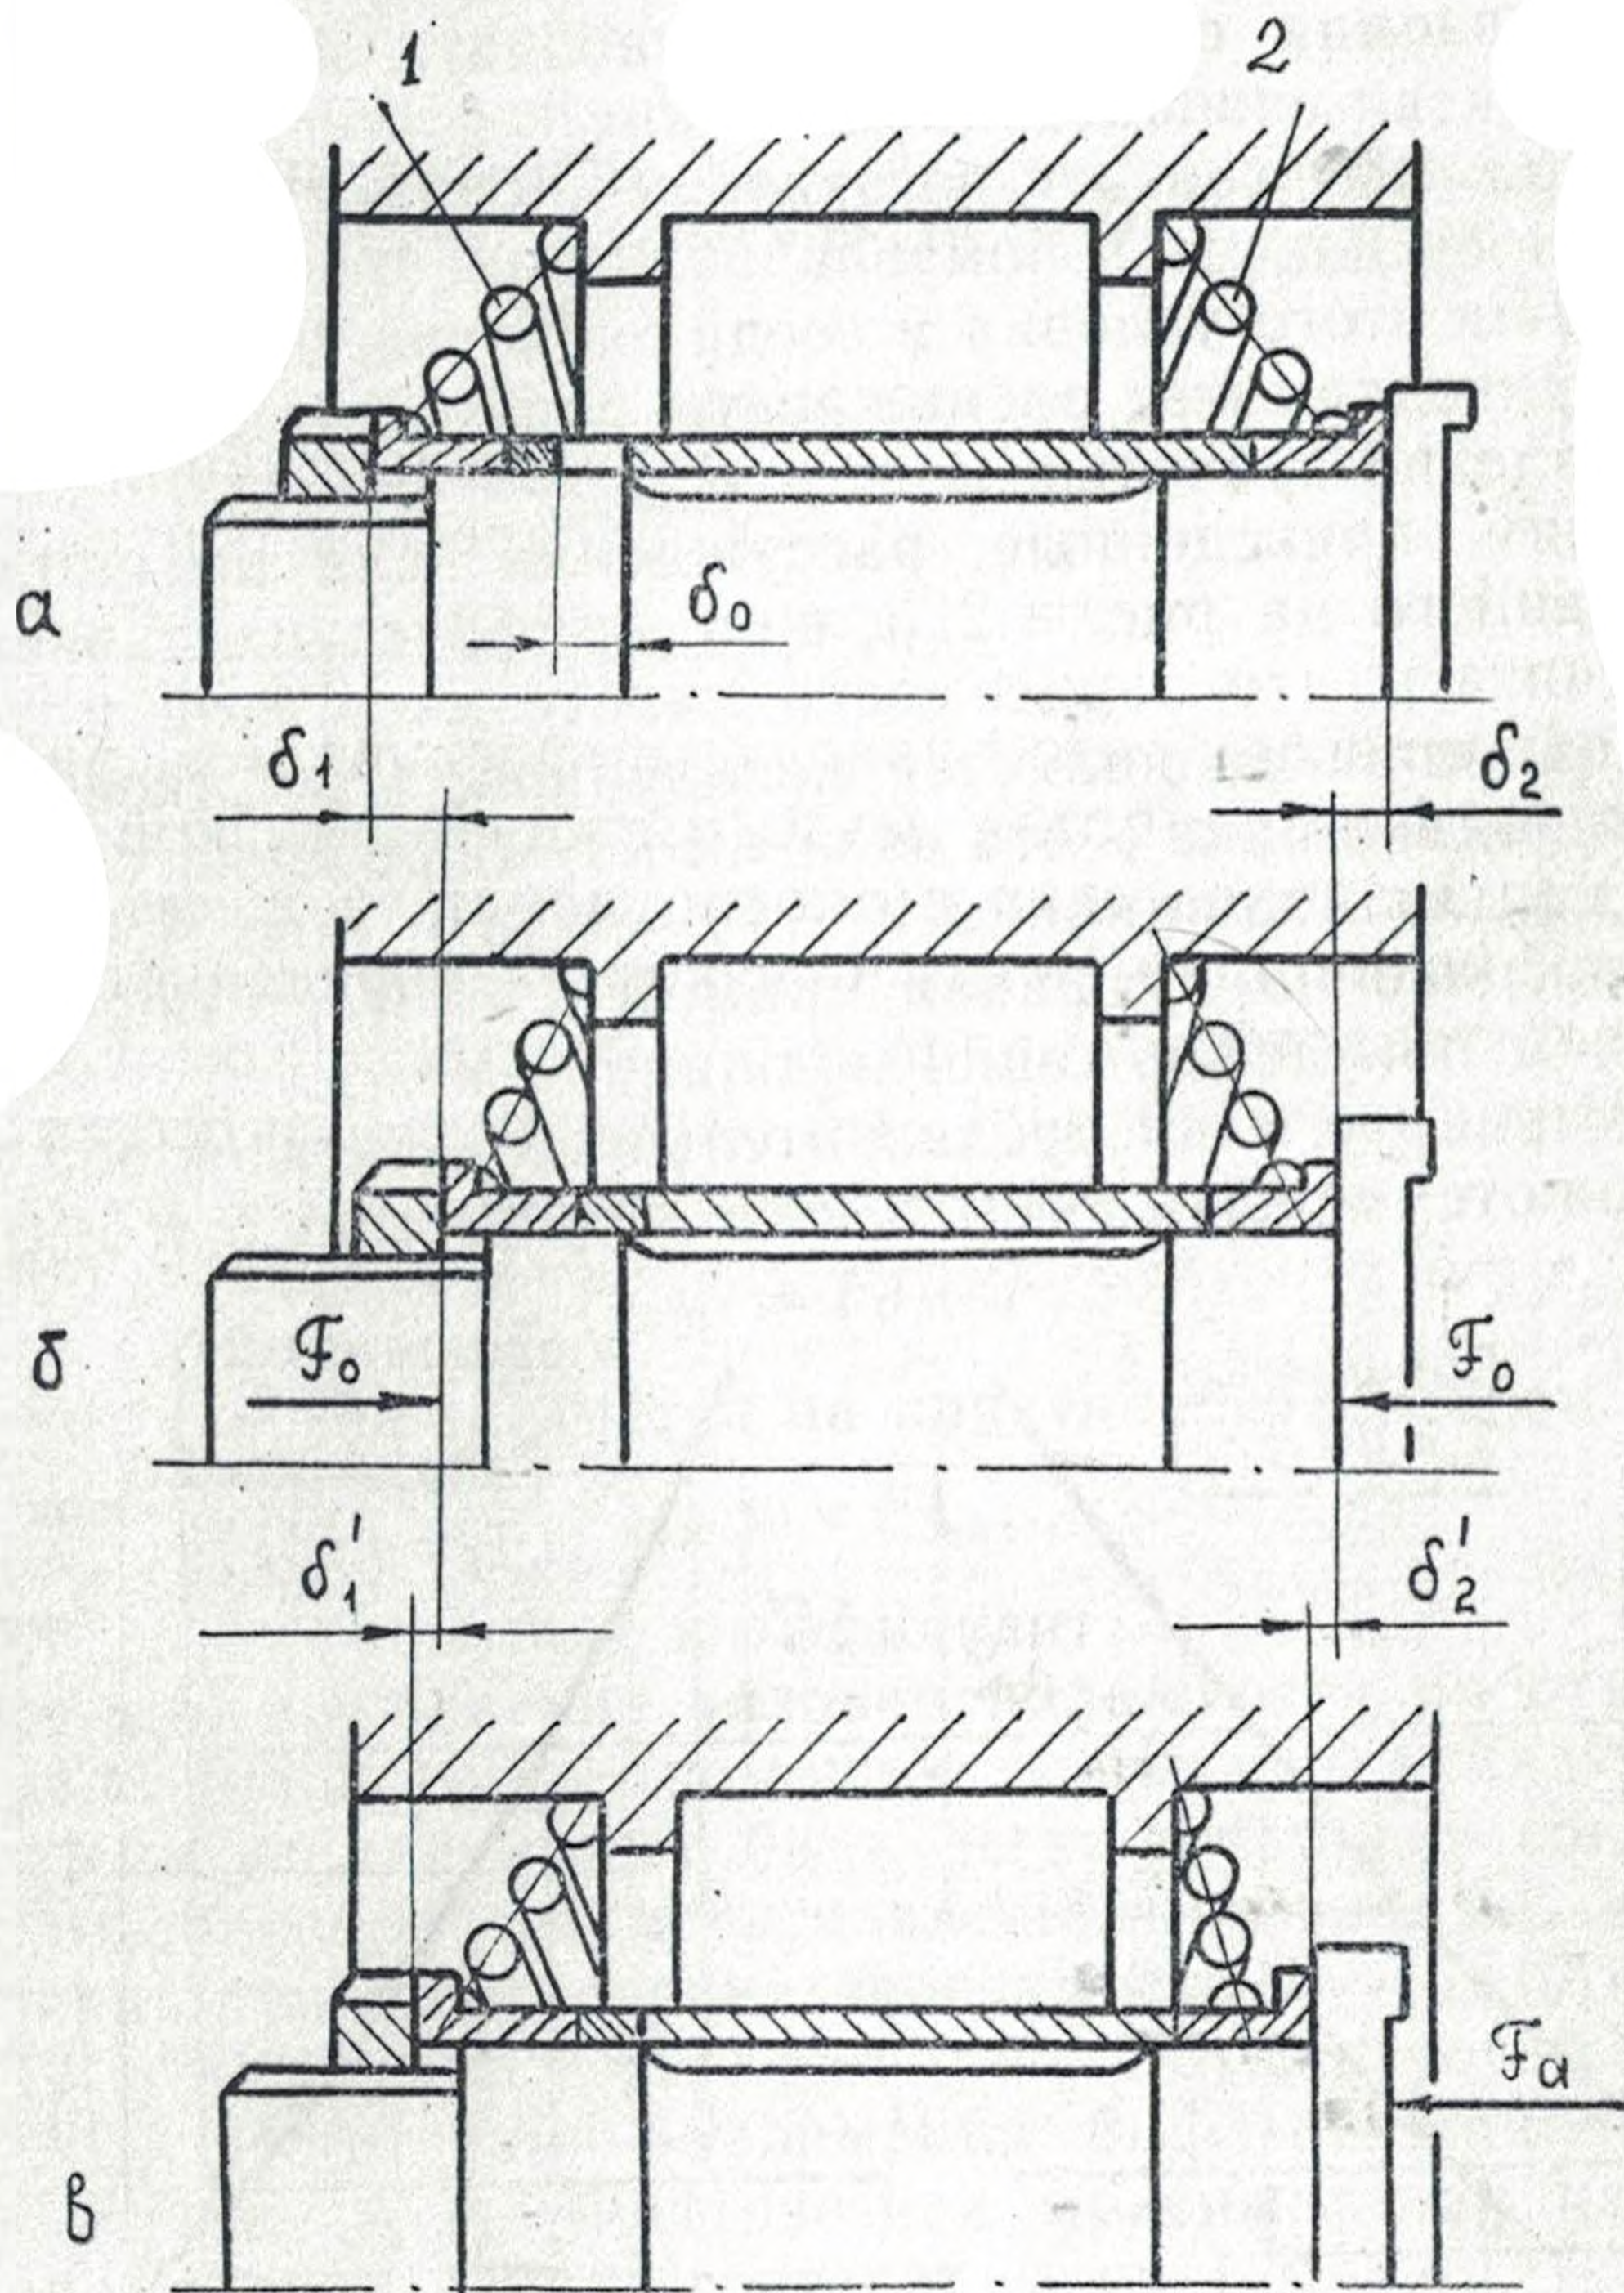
Упрощенная схема подшипникового узла: а — расположение деталей до затяжки гайки; б — расположение деталей после затяжки гайки; в — расположение деталей после приложения внешней нагрузки
